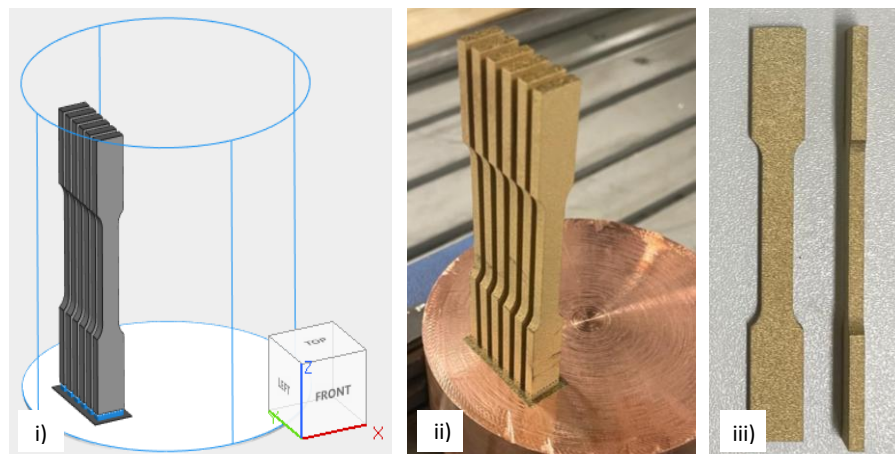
Provetes de tração impressos: i) modelação e posicionamento dos provetes no Materialise Magics, ii) conjunto de seis provetes pós-impressão e iii) provetes com os suportes de construção removidos.
